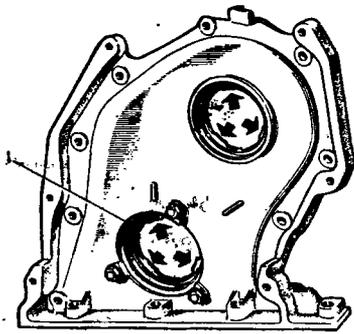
Крышка привода распределительного вала с держателем 1 переднего сальника коленчатого вала. Стрелками указаны выступы для центрирования держателя и крышки относительно коленчатого вала и валика привода масляного насоса
